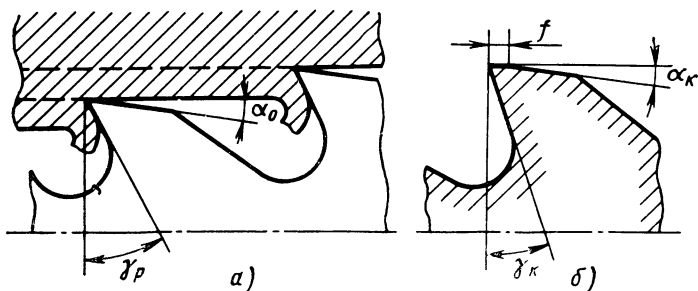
Профили режущих и калибрующих зубьев протяжки
